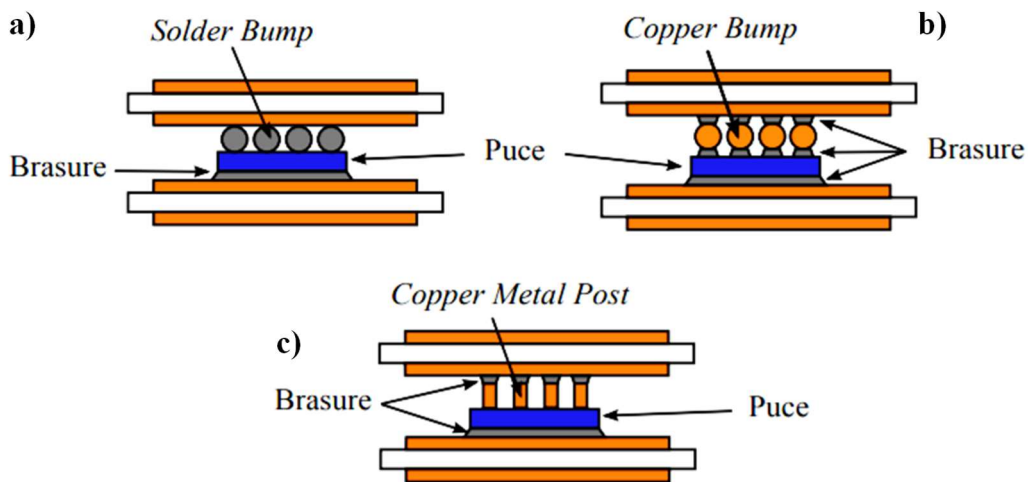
Exemples de technologies d'interconnexion sur la face avant : a) solder bump, b) copper bump, c) copper metal post [49]
